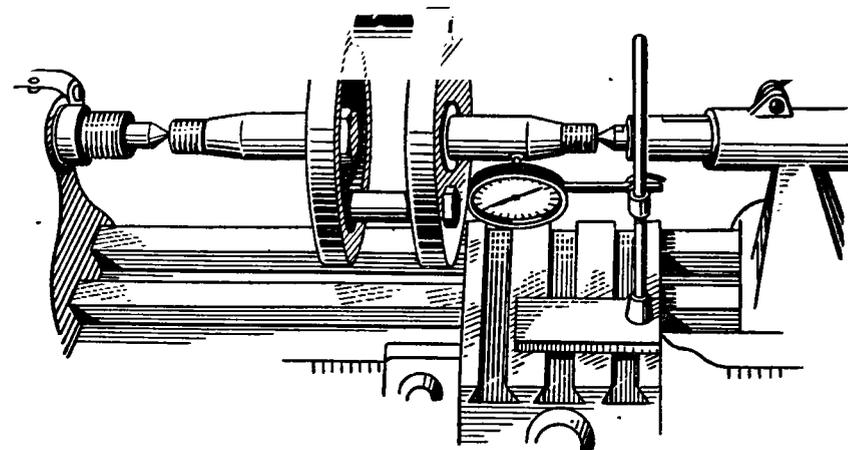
Проверка центровки коленчатого вала индикатором: 1—металлическая распорка.
